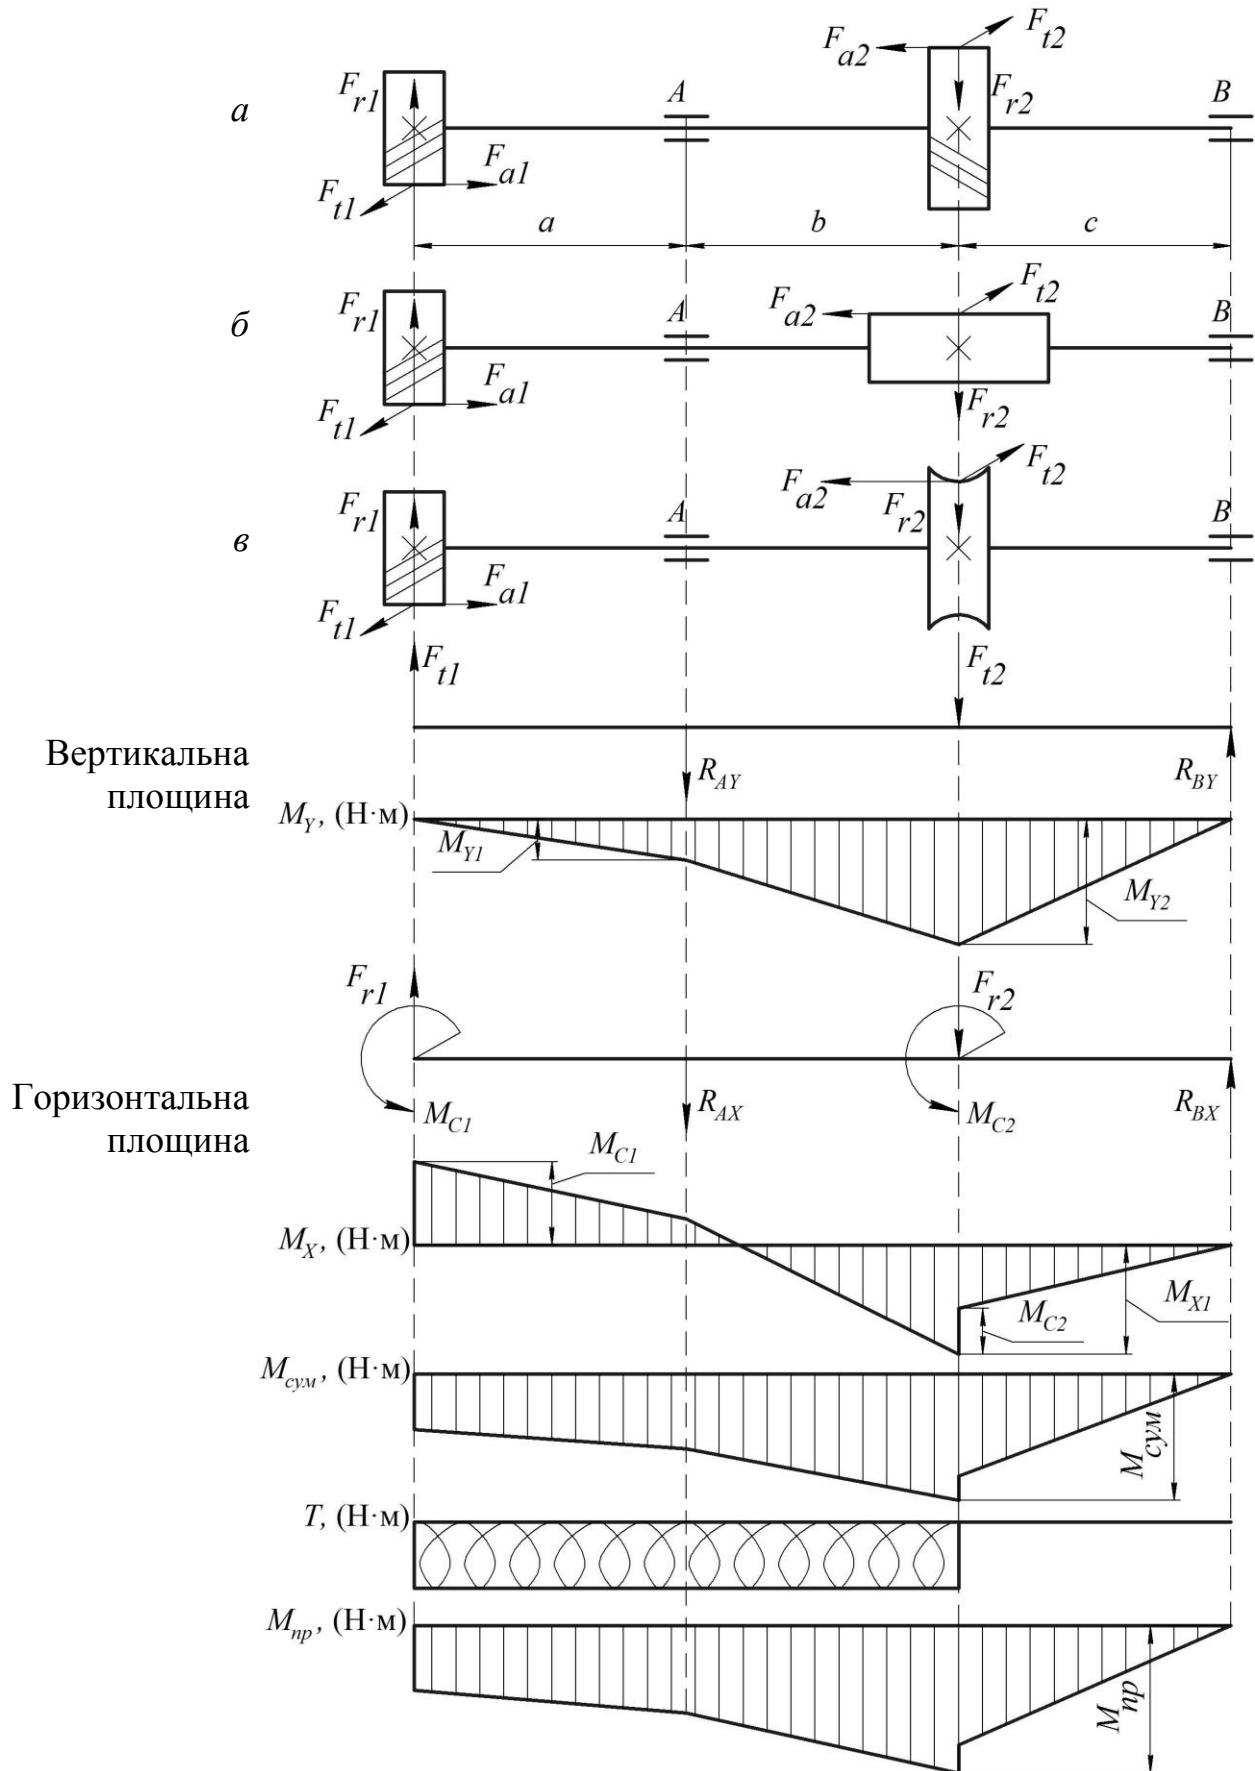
Проміжний вал двоступінчастого редуктора з консольним розташуванням зубчастого колеса
